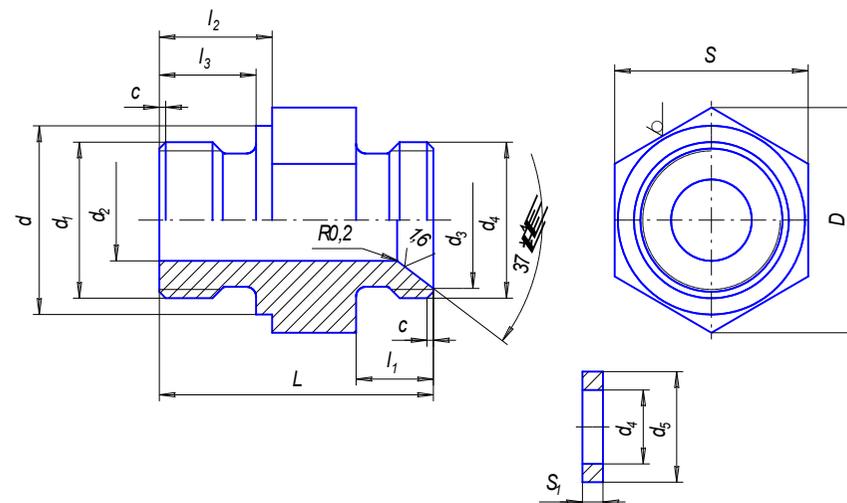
Штуцер нагнетательного трубопровода и уплотнительное кольцо
